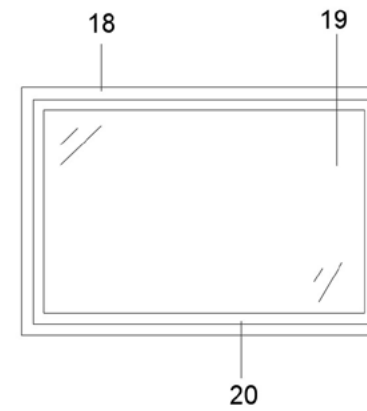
Detalle constructivo puerta de alacena con madera de pino
